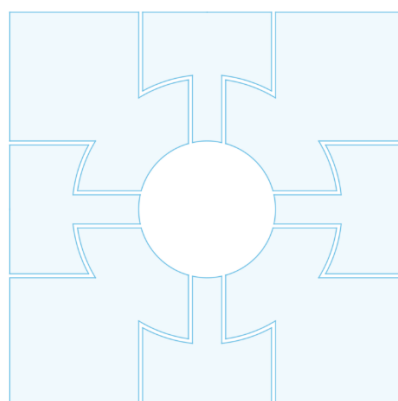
| Elaboración propia | Corte transversal con tolerancia entre las piezas
